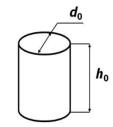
Образец для испытаний *Fig. 6. Test sample
